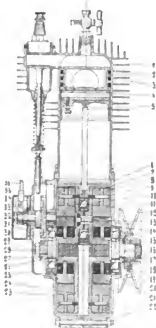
Dürckopp-Einzylindermotor, Totalschnitt.
